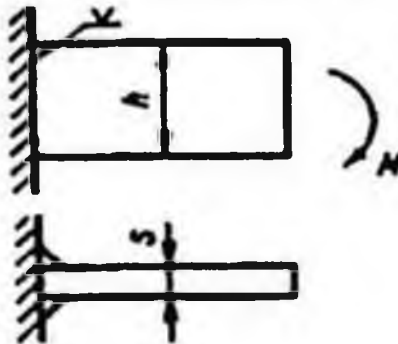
Сварное соединение кронштейна со стойкой двумя угловыми швами
